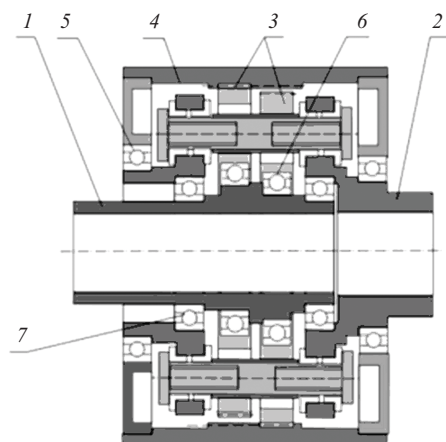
Схема конструктивного выполнения передачи К-Н-V: 1 – входной вал-водило; 2 – выходной вал (звено V); 3 – сателлиты; 4 – корпус, совмещенный с колесом внутреннего зацепления; 5 – подшипники корпуса; 6 – подшипники сателлитов; 7 – подшипники входного вала
